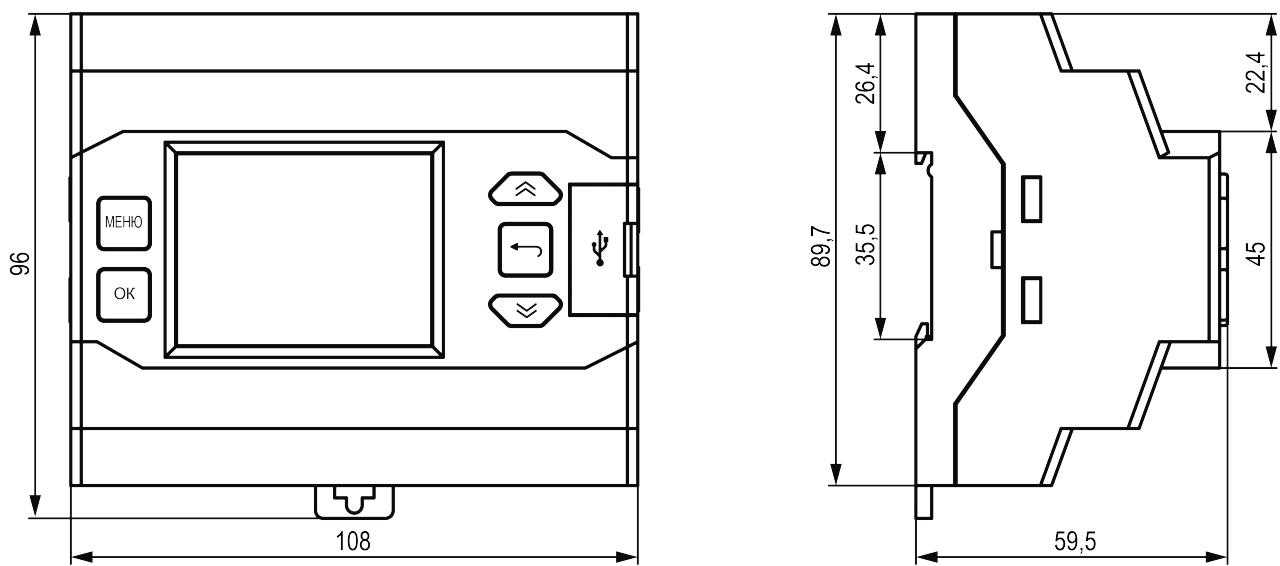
Габаритные и присоединительные размеры САУ-У2-Д6
